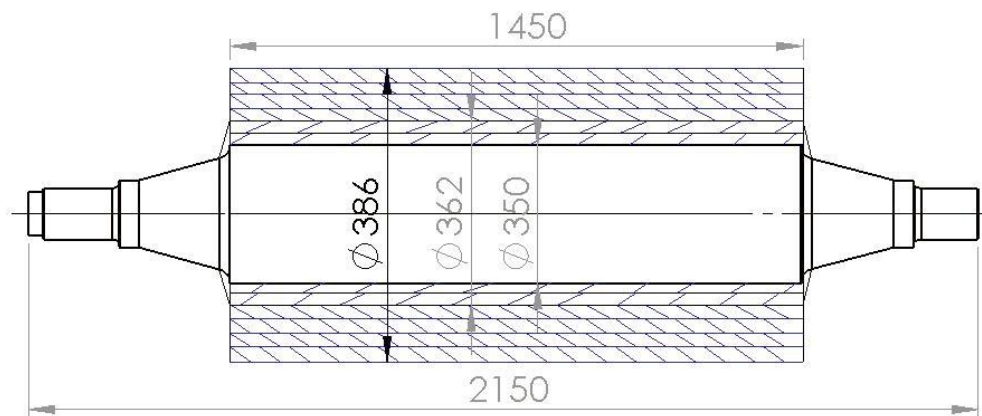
rechargement pièce $\text{Ø}386$ mm avec fil weld clad 03
